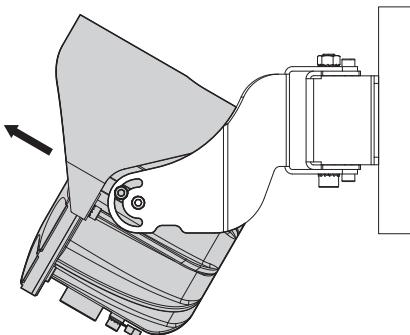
Installazione a parete (rotazione verticale, +30°).
